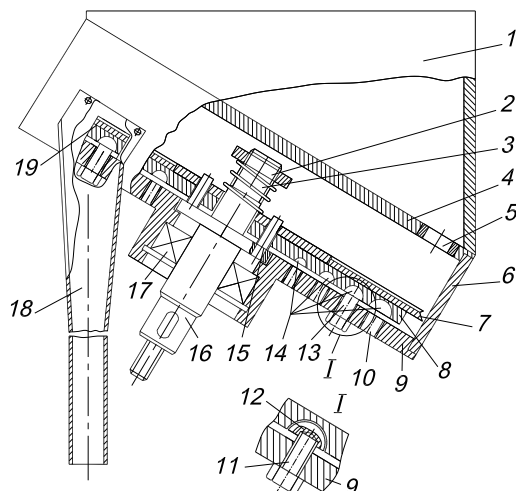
Конструктивна схема вібраційно-дисківий висівний апарат: 1 – бункер для насіння; 2 – гайка; 3 – пружина; 4 – ділильник; 5 – отвір дозувальний; 6 – банка; 7 – висівний диск; 8 – проміжний диск; 9 – основа; 10 – отвори; 11 – болт; 12 – опора сферичної форми; 13 – змінні опори; 14 – комірочки; 15 – штирі; 16 – приводний вал; 17 – підшипник; 18 – насіннепровід; 19 – бокове вікно
